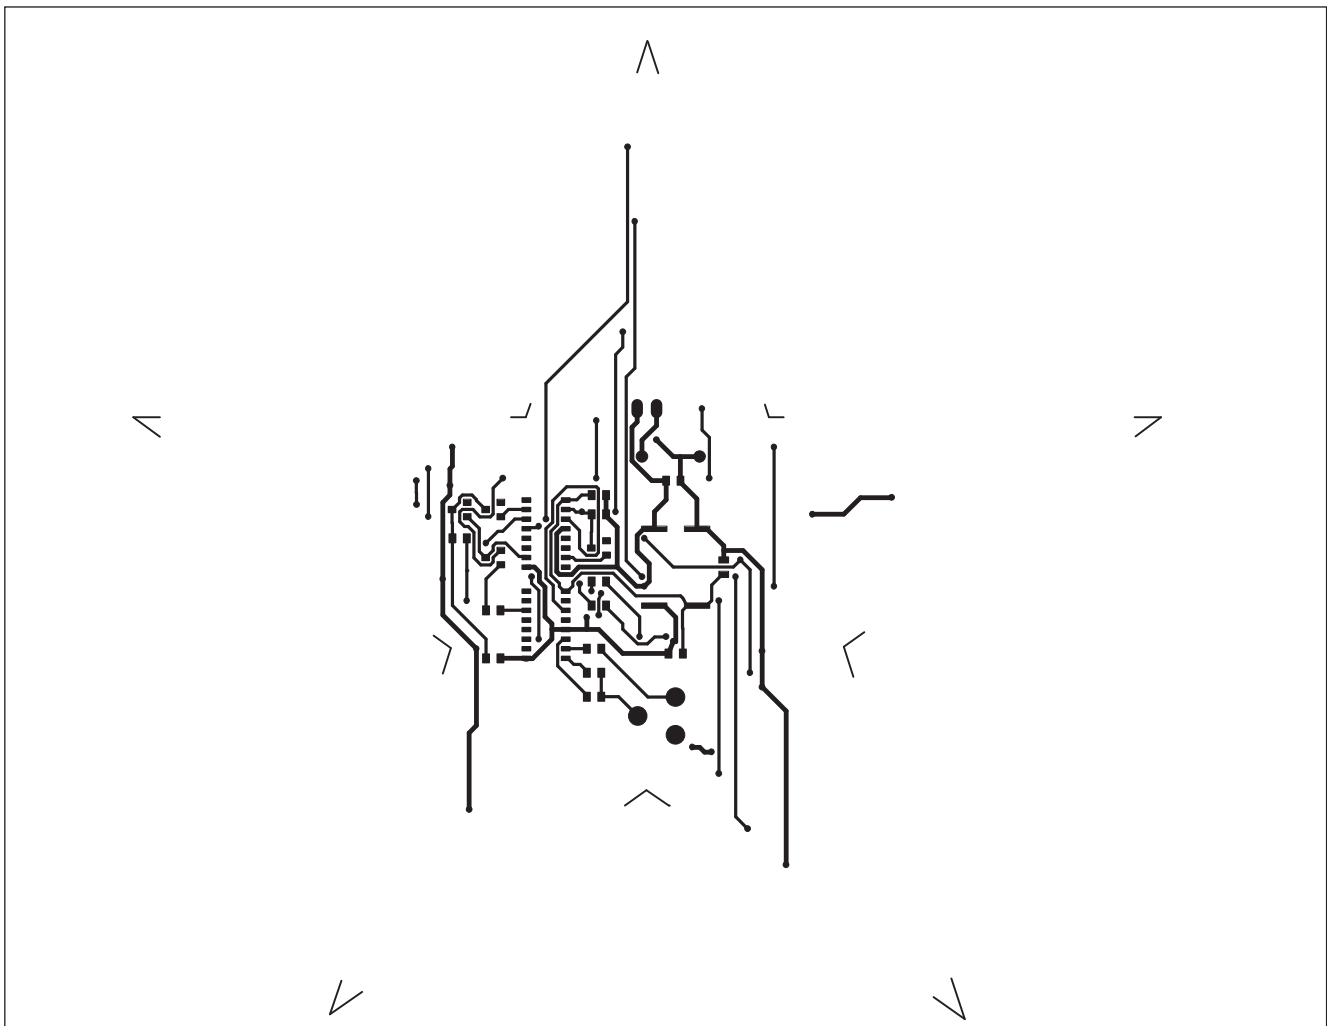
Rozložení součástí na desce hvězdy (strana BOTTOM)
